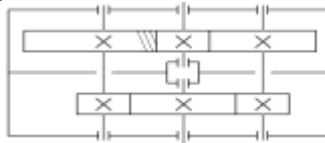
Кинематическая схема двухступенчатого соосного двухпоточного цилиндрического редуктора
